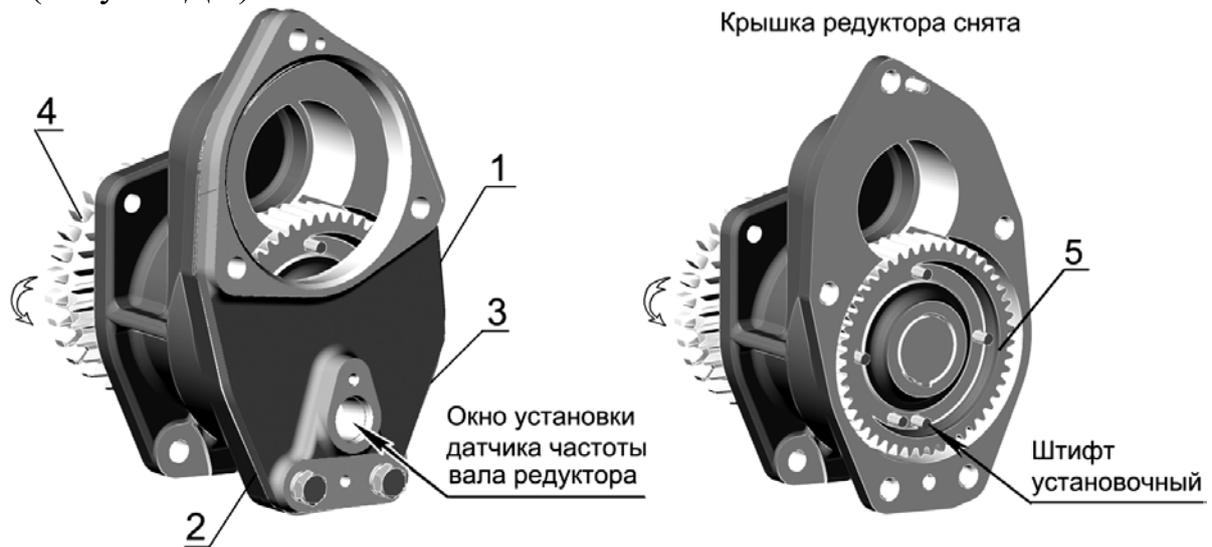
Установка датчика частоты вращения коленчатого вала
